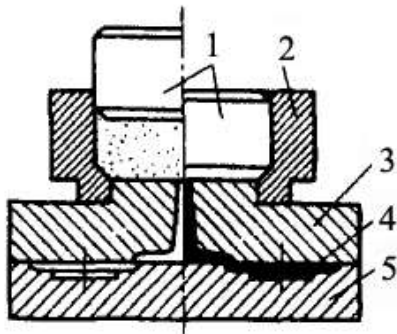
Схема литтєвого пресування полімерних композиційних матеріалів
